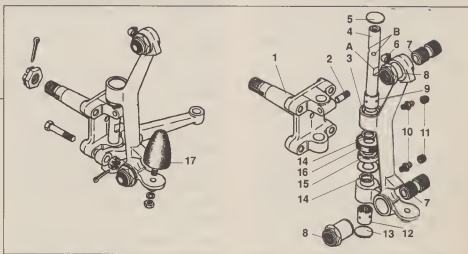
Стойки передней подвески и поворотные кулаки (слева – в сборе): 1 – поворотный кулак; 2 – штифт; 3 – стойка; 4 – шкворень; 5 – верхняя заглушка; 6 – пресс-масленка; 7 – распорные резьбовые втулки; 8 – резьбовые втулки; 9 – верхний подшипник шкворня; 10 – пресс-масленки; 11 – колпачки пресс-масленок; 12 – нижний подшипник шкворня; 13 – нижняя заглушка; 14 – защитные кольца подшипника; 15 – подшипник; 16 – защитный колпачок подшипника; 17 – буфер хода сжатия. А – лыска под ключ; В – выемки под штифт.
